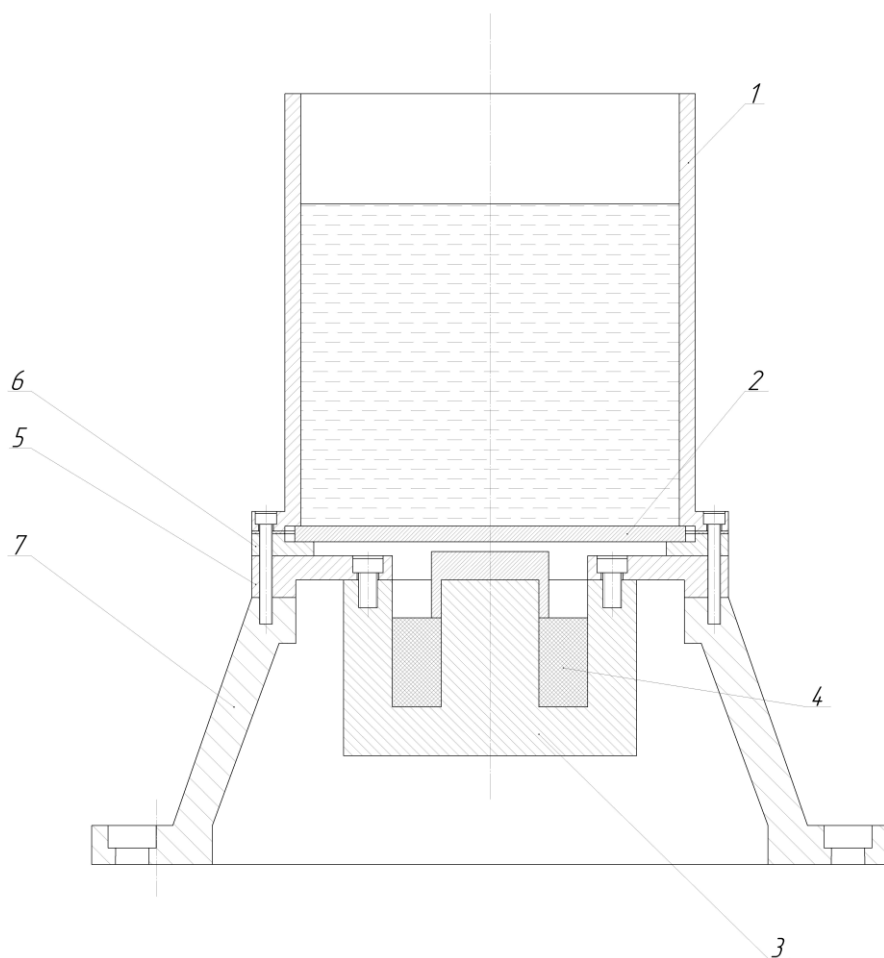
Конструкция предлагаемой установки для мойки деталей и узлов легкового автомобиля
